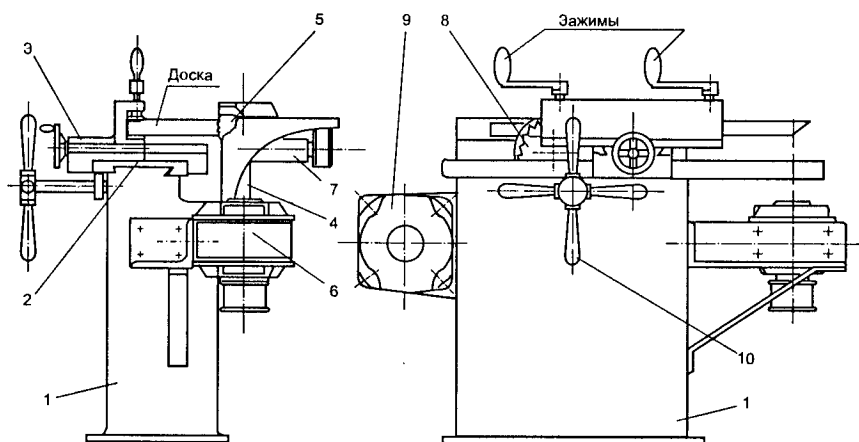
Общий вид станка для изготовления клиньев: 1 — литая станина, 2 — салазки горизонтального хода, 3 — салазки поперечного хода, 4 — вал фасонной фрезы, 5 — фасонная фреза, 6 и 9 — электродвигатель, 7 — вал дисковой пилы, 8 — дисковая пила, 10 — штурвал
